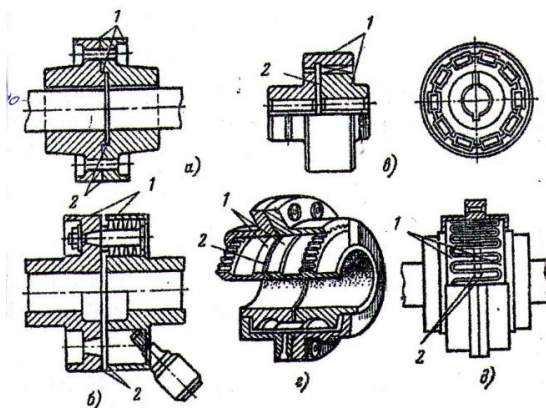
Види муфт для з'єднання валів електричних машин: а – жорстка фланцева; б – втулко-пальцева; в – пружна з резиновими пластинами; г – зубчаста; д – змінної жорсткості (пружинна); 1, 2 – точки заміру радіального та торцевого биття
